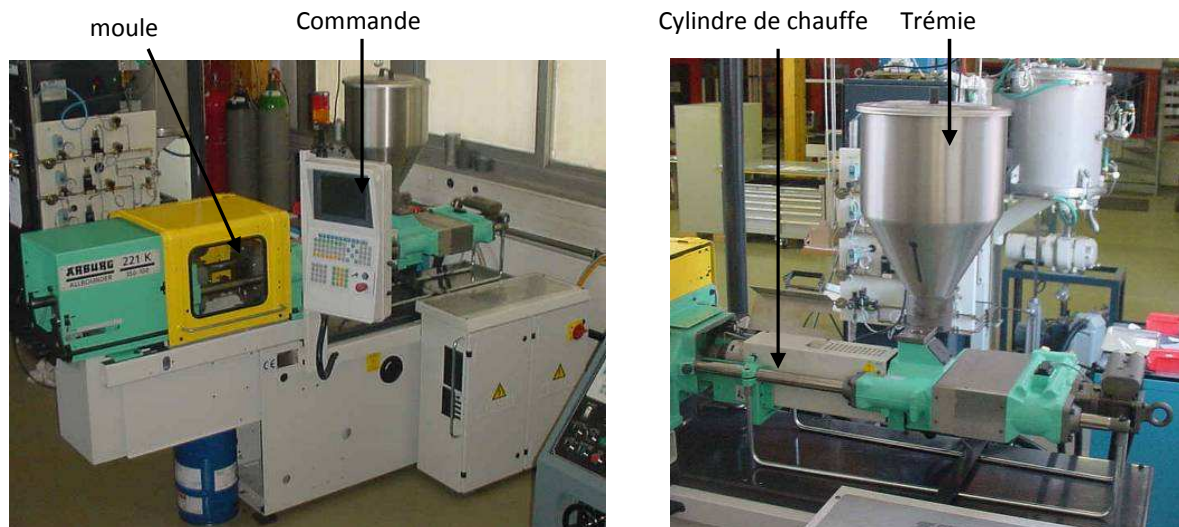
Presse à injecter ARBURG 221K (vue moule et unité d'injection)
